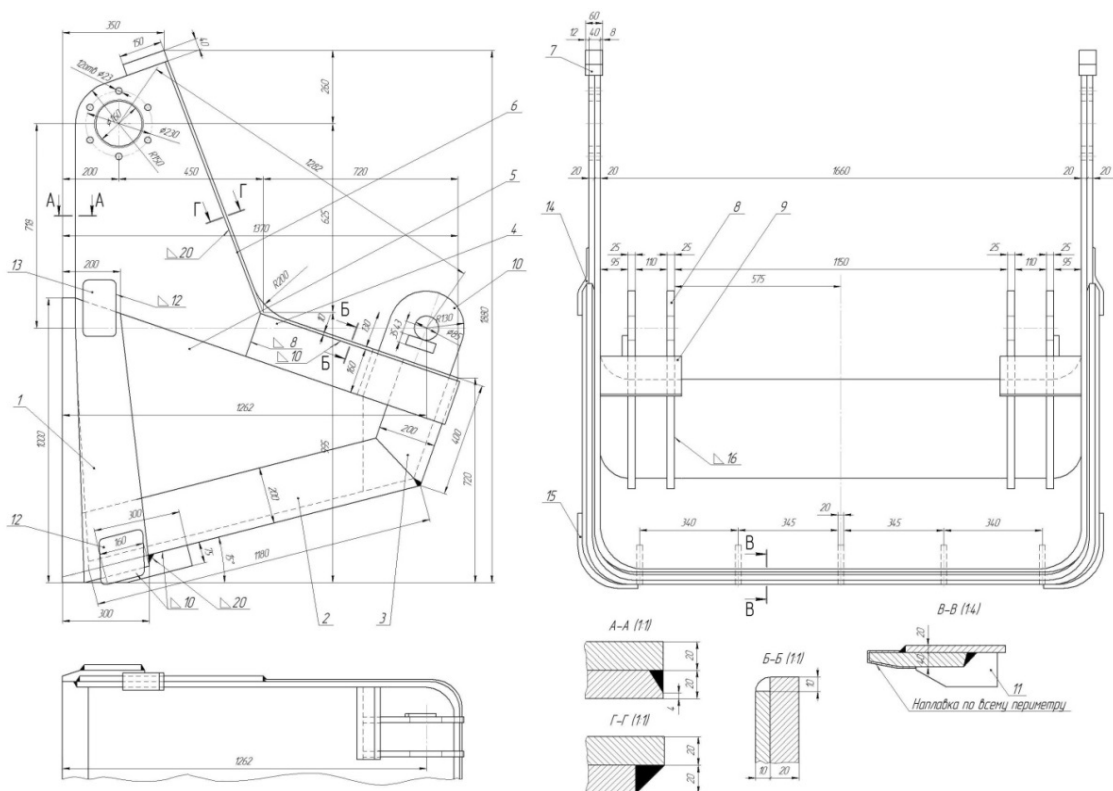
Ковш грейфера: 1 - ніж; 2 - днище; 3 - задня стінка; 4 - смуга; 5 - бічний лист; 6, 7 - підкладки; 8 - вуха; 9 - смуга; 10 - планка; 11 - ребро; 12, 13 - накладка ліва; 14, 15 - накладка права
